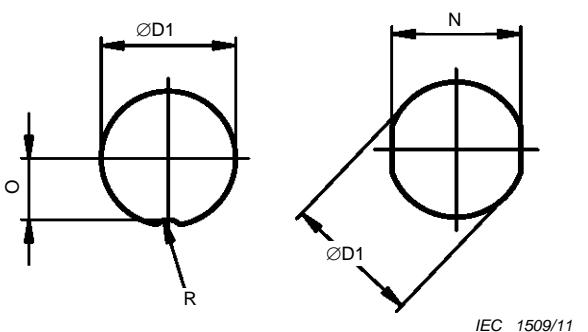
Dimensions – Plan de découpe des panneaux IP65/67
